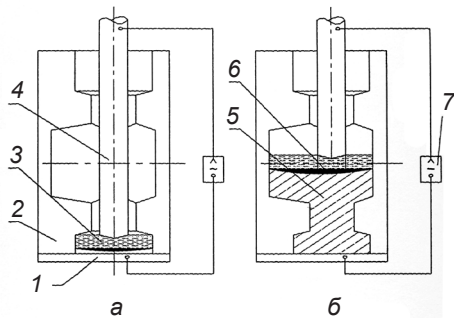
Схема ЭШЛ заготовки корпуса задвижки с фланцами на концах патрубков: начало процесса (а), выплавка центральной части (б); 1 – поддон, 2 – кристаллизатор, 3 – шлаковая ванна, 4 – расходный электрод, 5 – выплавляемая заготовка, 6 – металлическая ванна, 7 – источник питания
